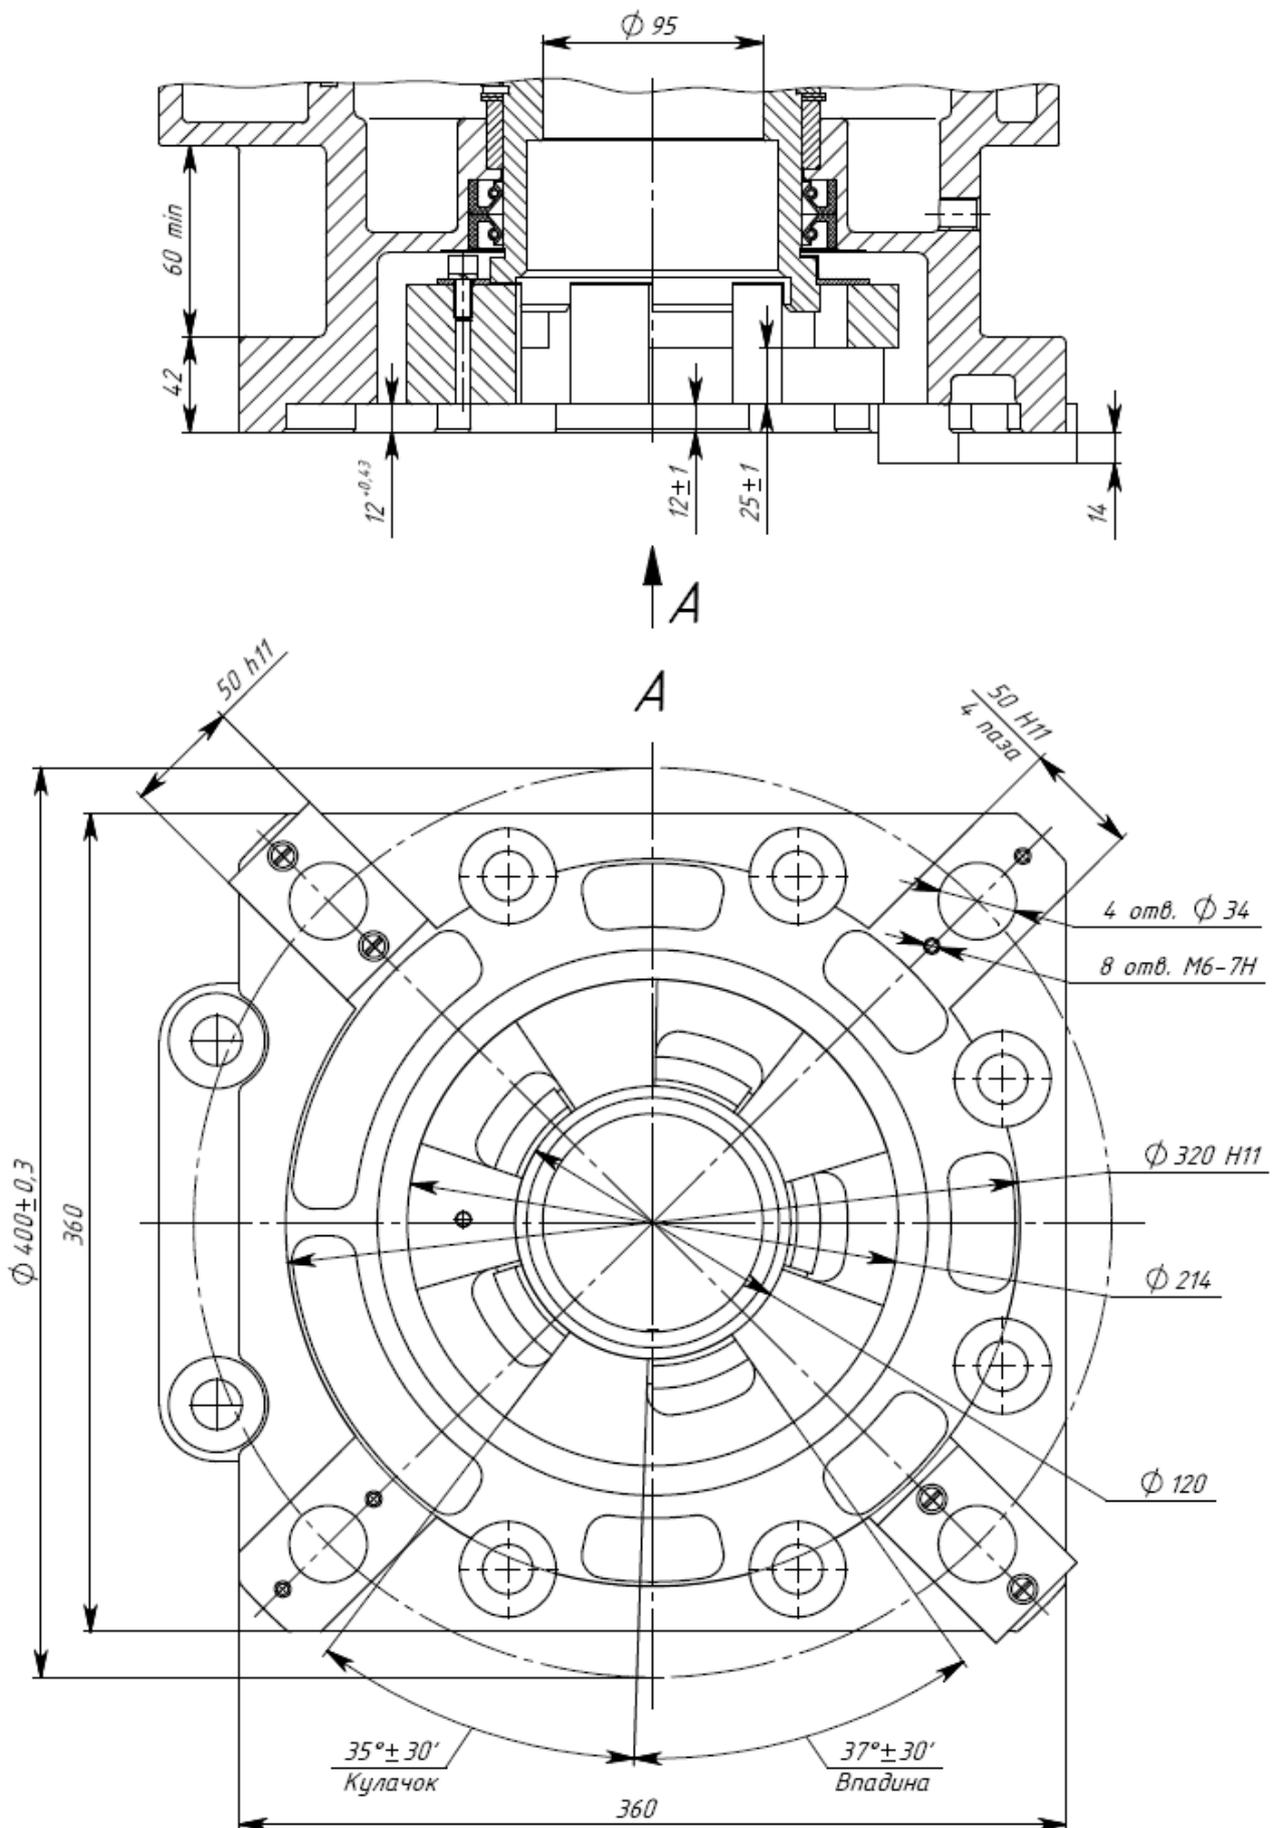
Присоединение типа Д для конструктивной схемы 43
